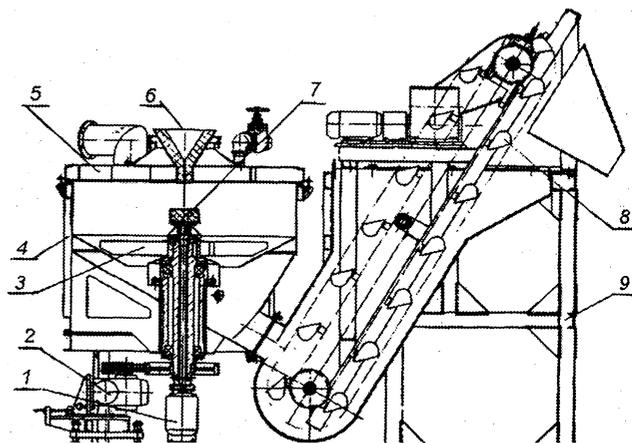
Схема дробелитейной машины: 1, 2 – привод; 3 – крыльчатка; 4 – корпус; 5 – крышка; 6 – воронка; 7 – гранулятор; 8 – элеватор; 9 – рама
